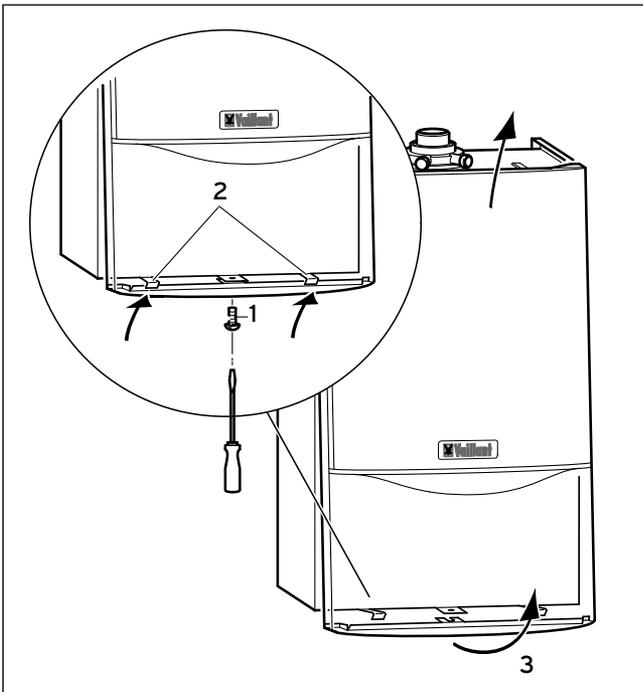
Geräteverkleidung abnehmen/anbringen
